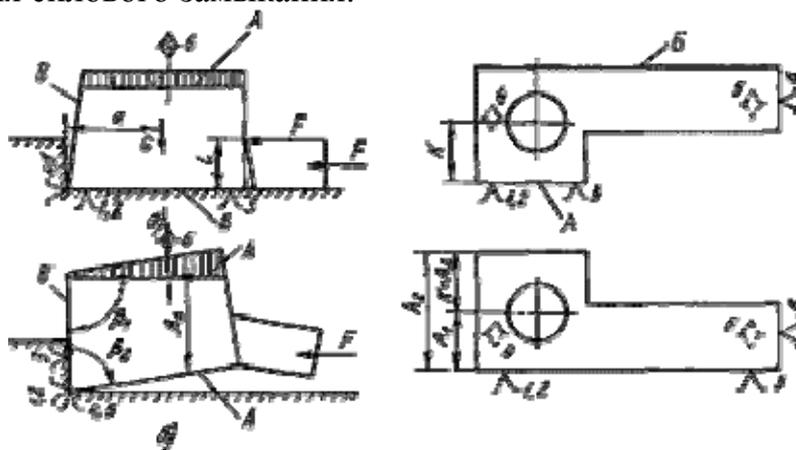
Смена баз у заготовок: а) неорганизованная, б) организованная
